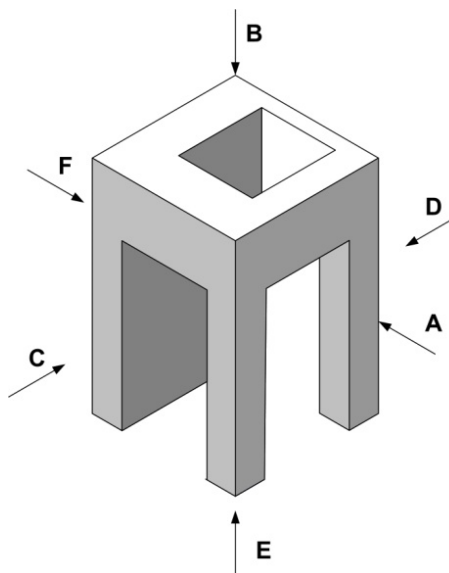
Imagen de la observación exterior de un objeto arquitectónico. Fuente realizado por la autora.
